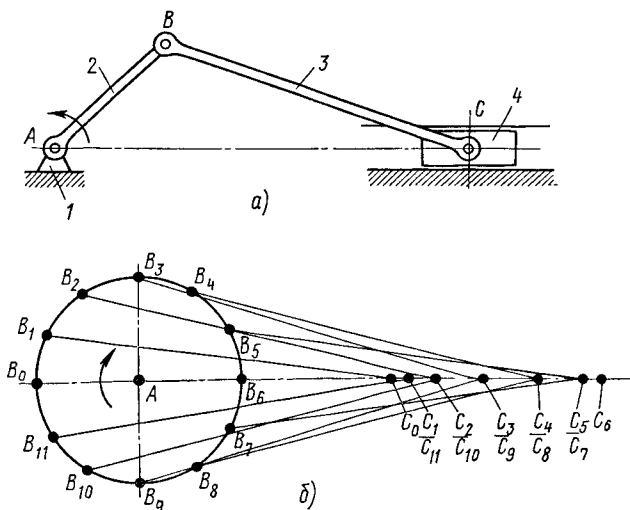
Схемы кривошипно-шатунного механизма (а) и определения неравномерности движения ползуна (б)
